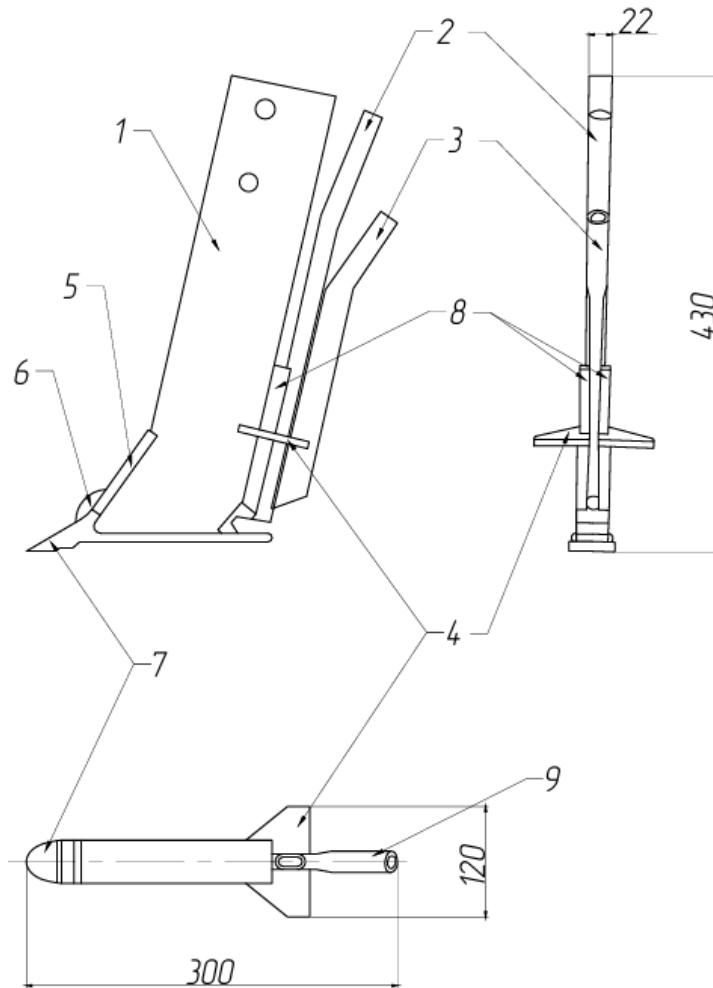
Туковий ніж: 1 – передня різальна кромка; 2 – упор; 3 – трубка для рідких добрив; 4 – пластина; 5 – приймач для шланга; 6 – формуючий елемент; 7 – носок ножа; 8 – тукопровід; 9 – вихідна трубка тукопроводу
